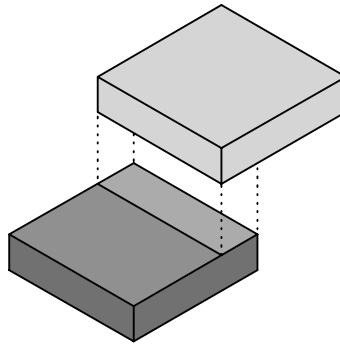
Explosionszeichnung des Druckscherprüfkörpers. Eine Platte aus Glas wurde auf eine Platte aus Metall mit einer definierten Überlappungslänge geklebt. Verwendet wurden die beiden Klebstoffe Photobond 4468 und Photobond GB485.
